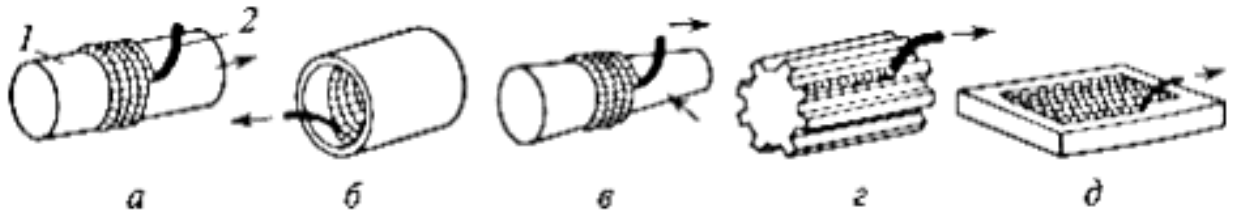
Схеми вібродугового наплавлення зношених поверхонь:
